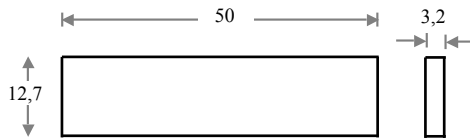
Dimensiones en mm de una probeta rectangular para ensayos mecánicos de flexión.
